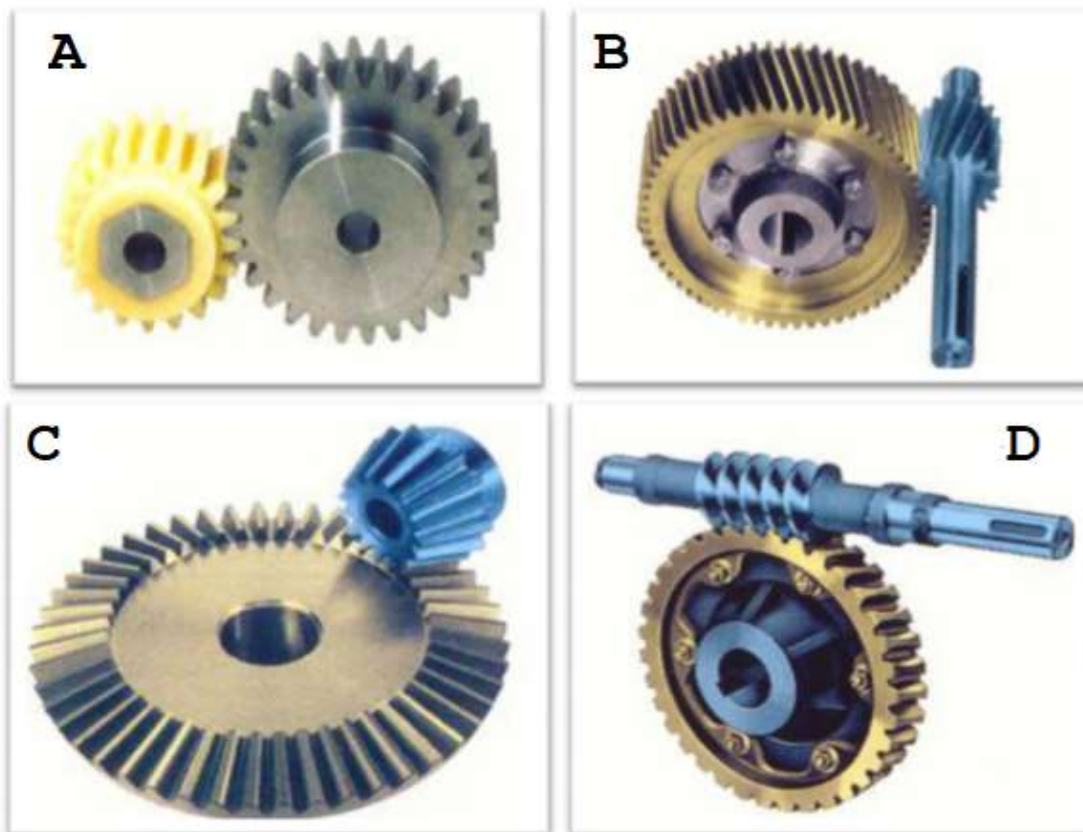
4 : Les Types d'engrenages utilisés dans l'industrie : (A) Engrenage parallèle, (B) Engrenage hélicoïdal, (C) Engrenage conique et (D) Roue et vis sans fin.
